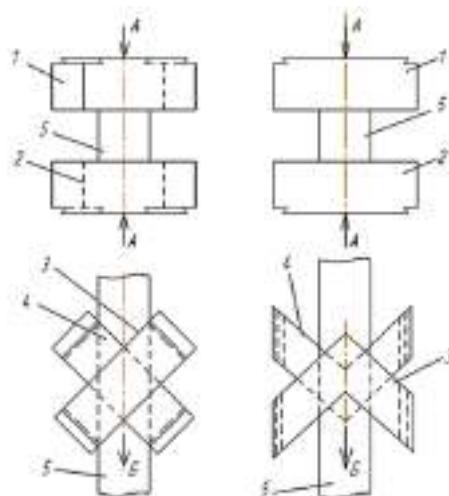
Схема устройства для ковки заготовок с непрямолинейным фронтом подачи
